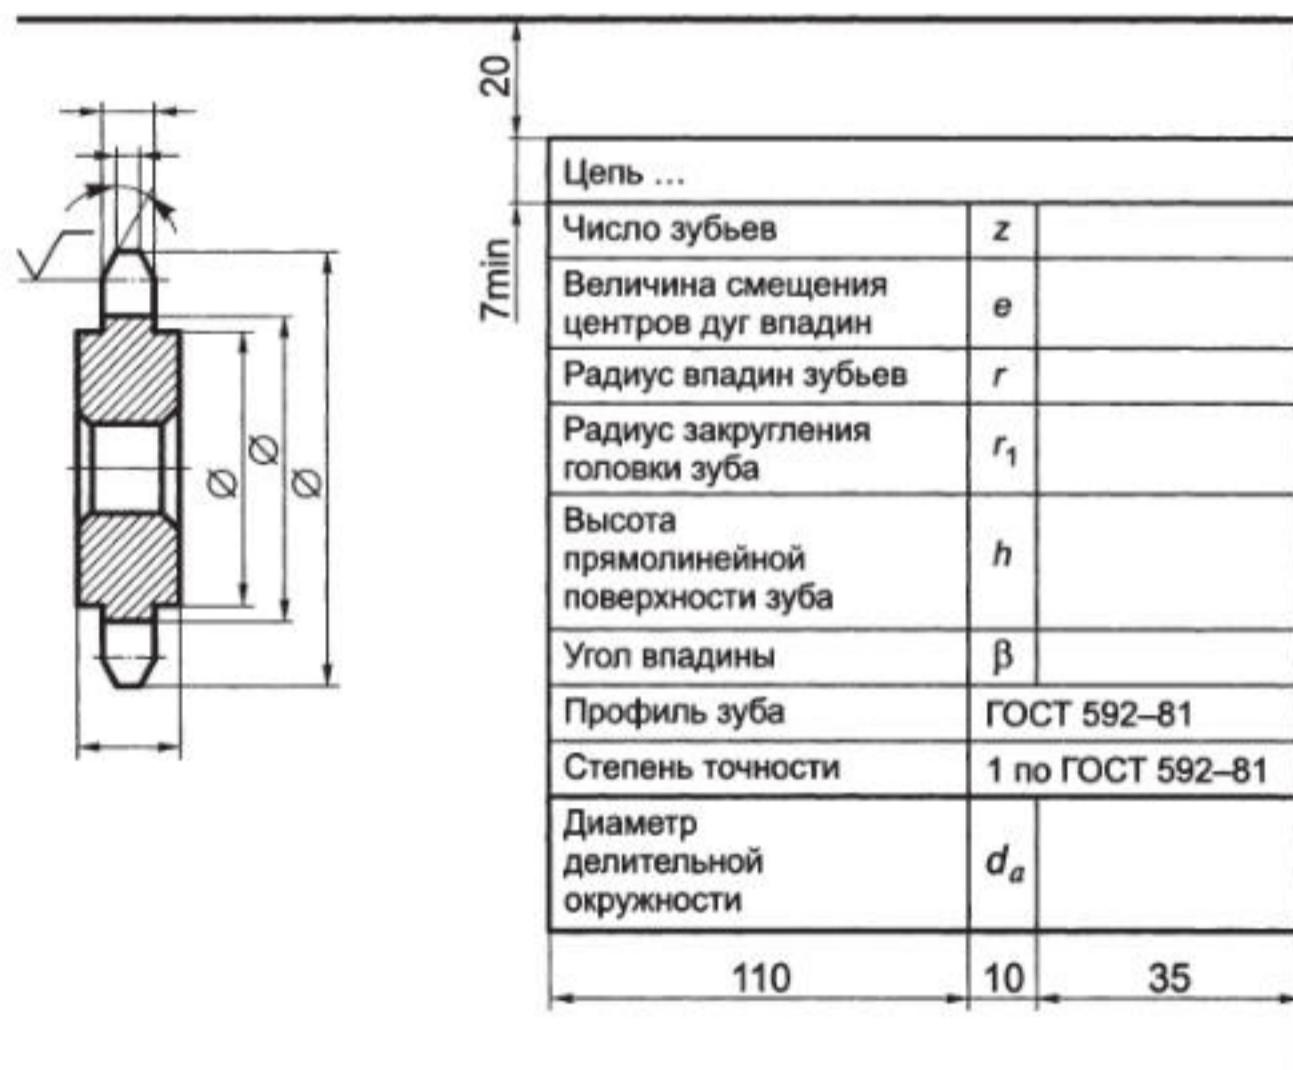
Пример чертежа звездочки для пластинчатых тяговых цепей
